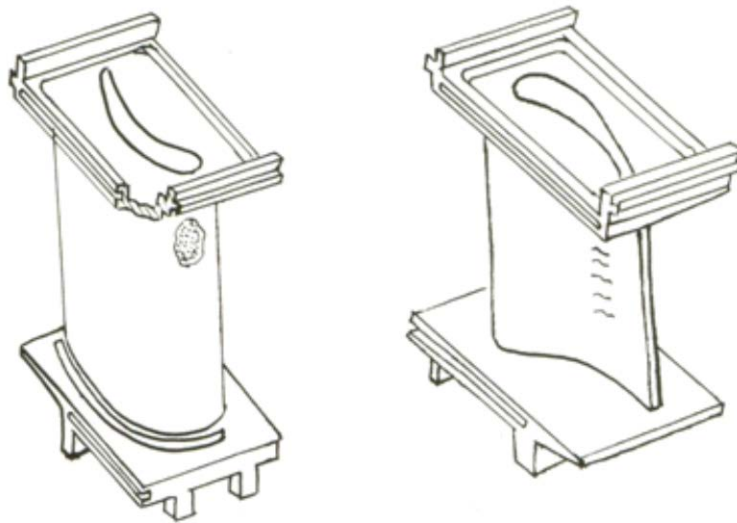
Внешний вид лопаток 1-го соплового аппарата двигателя НК-22
